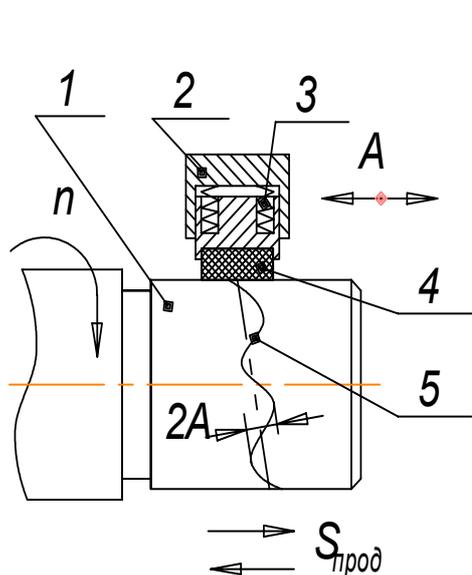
Схема суперфиниширования поверхности: 1 – заготовка; 2 – корпус инструмента; 3 – пружины; 4 – абразивный брусок; 5 – траектория относительного движения инструмента; n – частота вращения заготовки; $S_{прод}$ – подача осевая; $2A$ – амплитуда относительного движения инструмента
